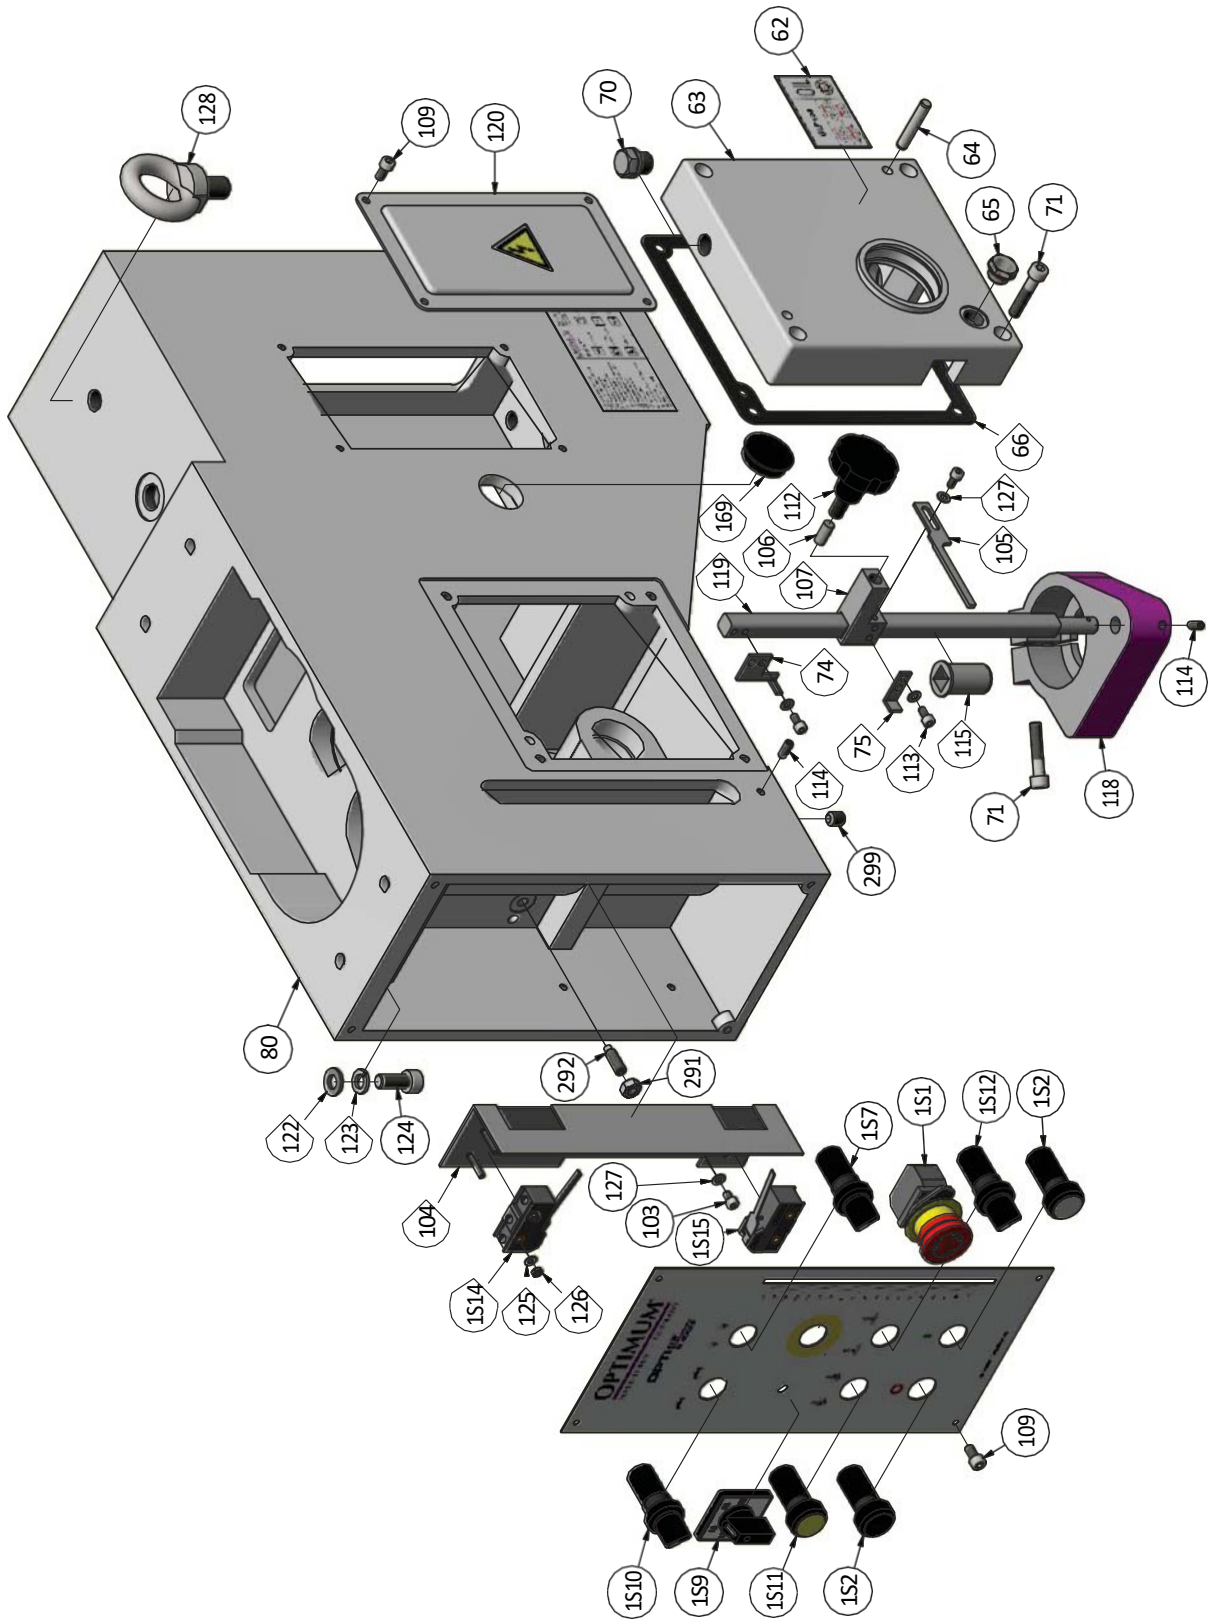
Vorschubgetriebe 3 von 4 - Gearbox 3 of 4
